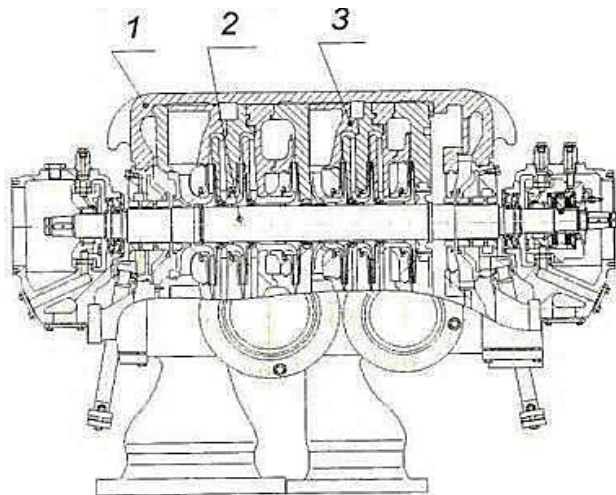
Базовий корпус з горизонтальним роз'ємом УВКМ другого покоління:
